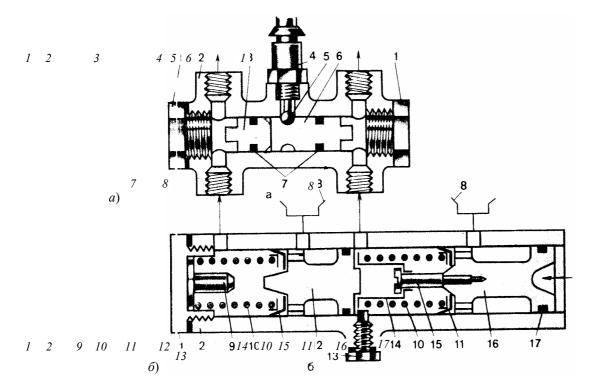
Схема аварийного сигнализатора (a) и главного тормозного цилиндра (δ) автомобиля УАЗ-3303:
